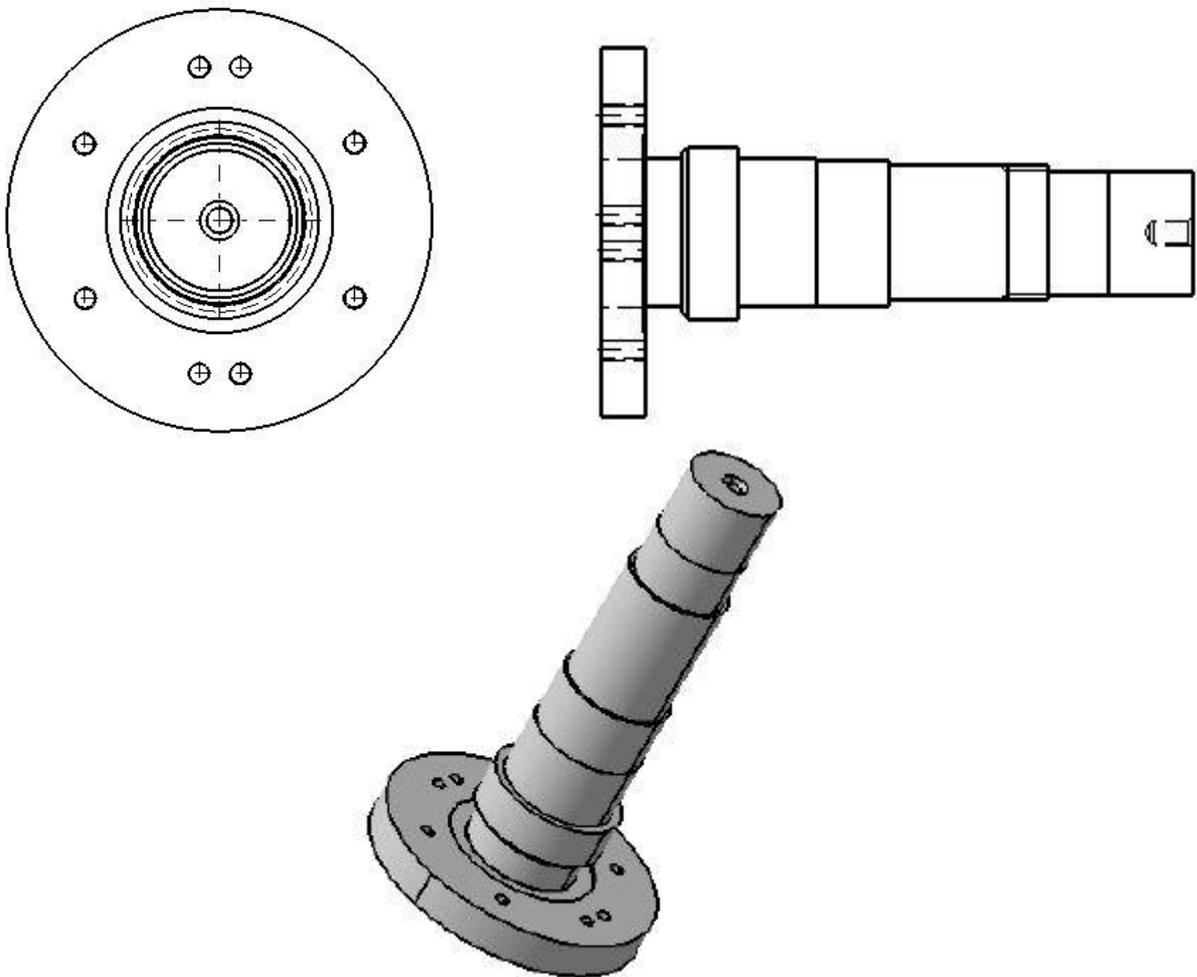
1 : Dessin de l'arbre axe bobinoir
